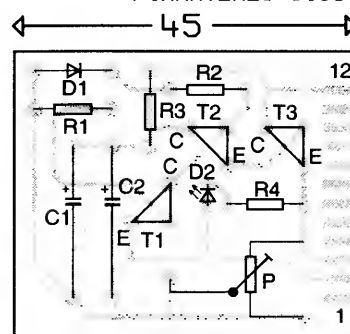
Deska s plošnými spoji obvodu z obr. 28
